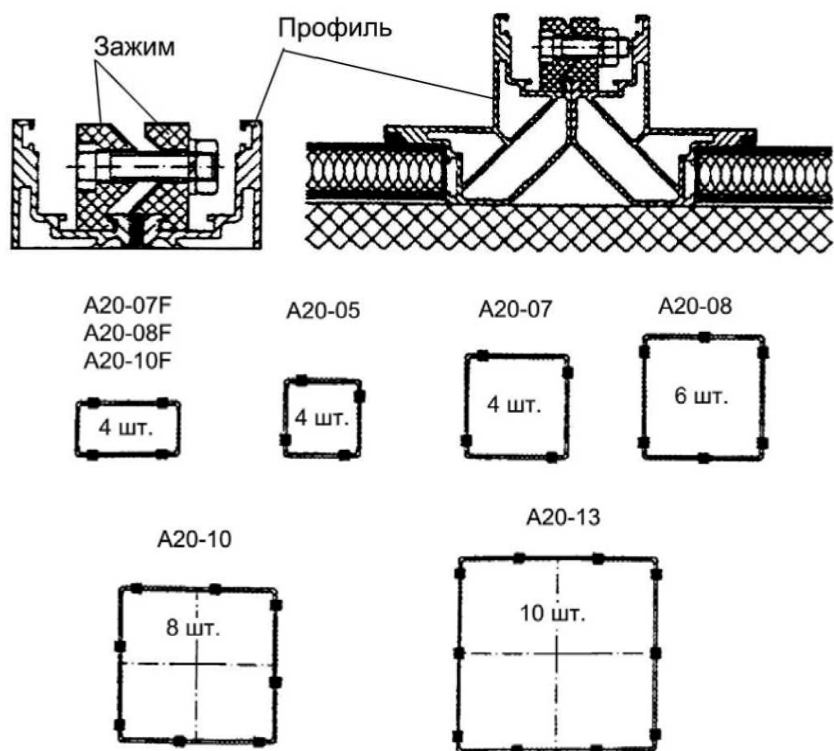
Соединение секций установок с ал.профилем каркаса и толщиной стенки 20мм
